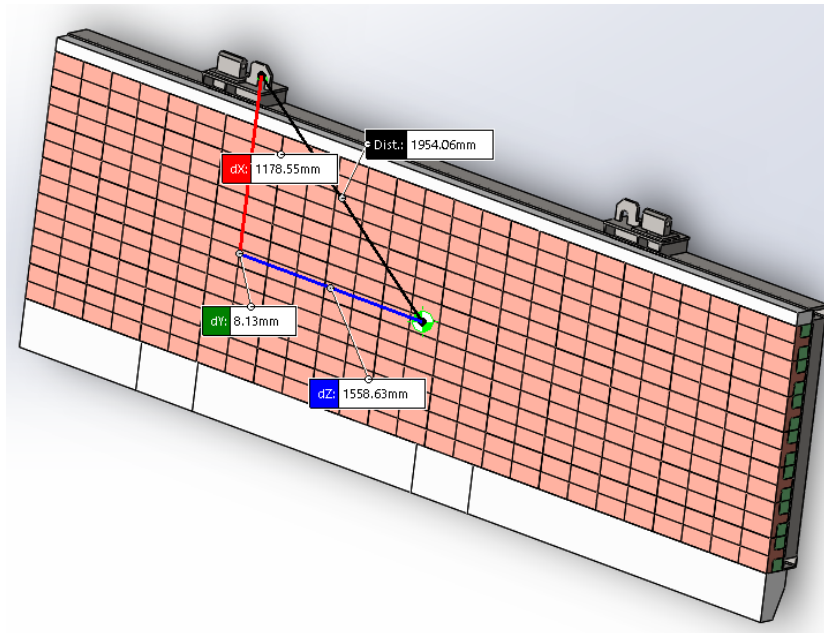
Centro de massa na parte estrutural da porta seca alterada.
